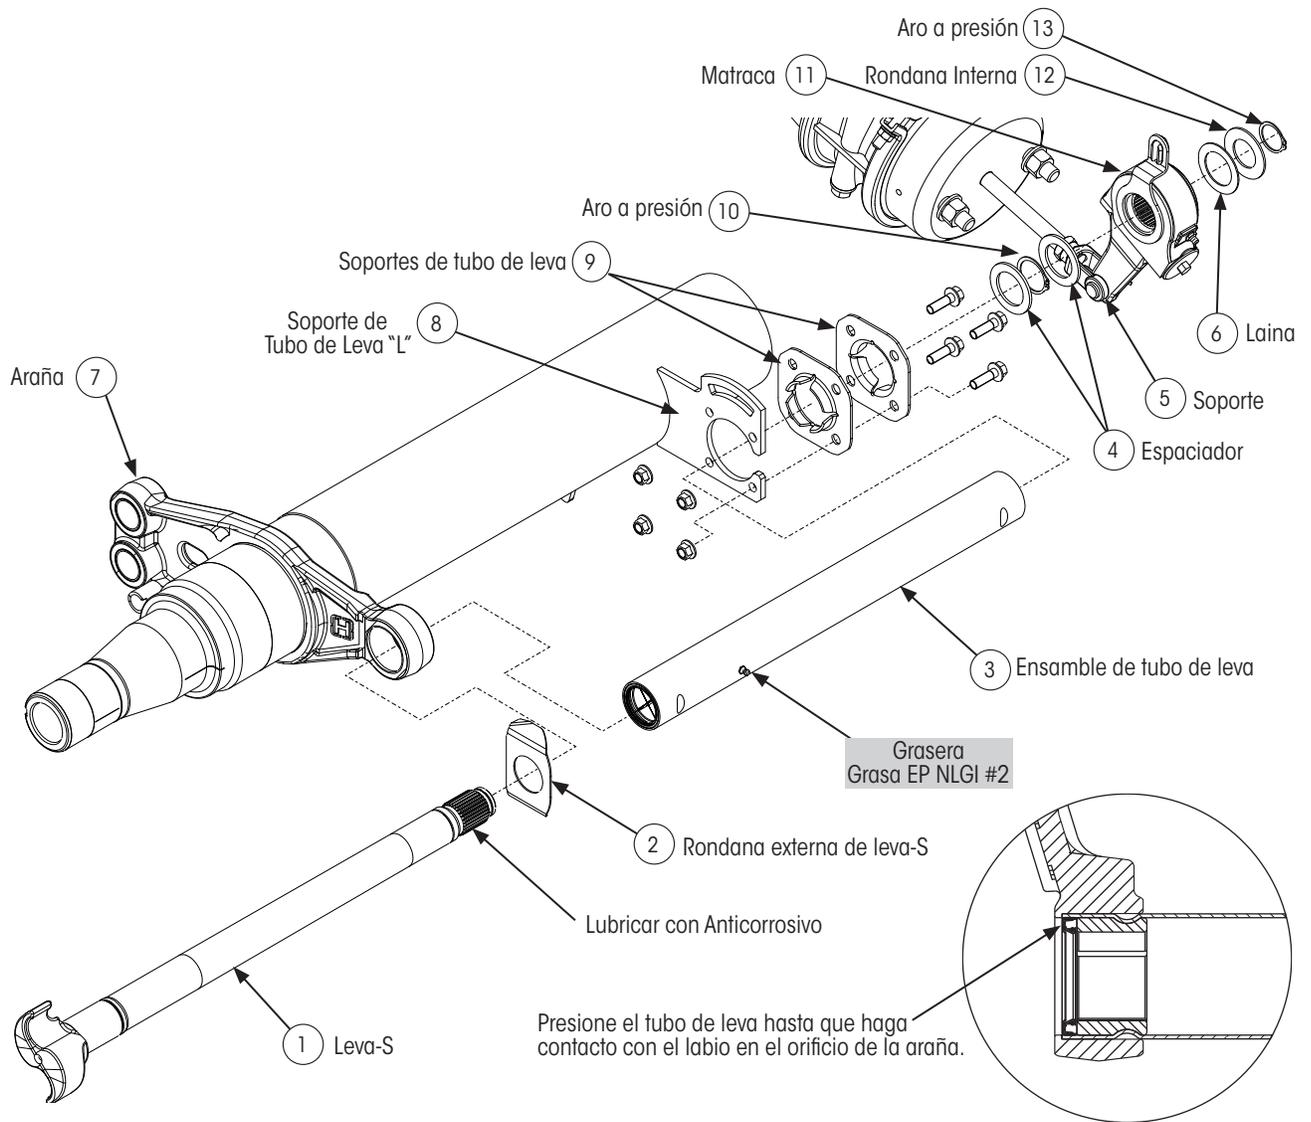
Ensamble de tubo de leva de montaje soldable TRLAXLE®
